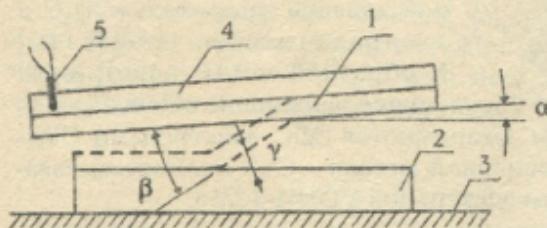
Схема сварки взрывом: 1 - метаемая пластина - сталь 08Х25Г15С; 2 - основной металл - Ст. 3; 3 - опора; 4 - взрывчатое вещество; 5 - детонатор
